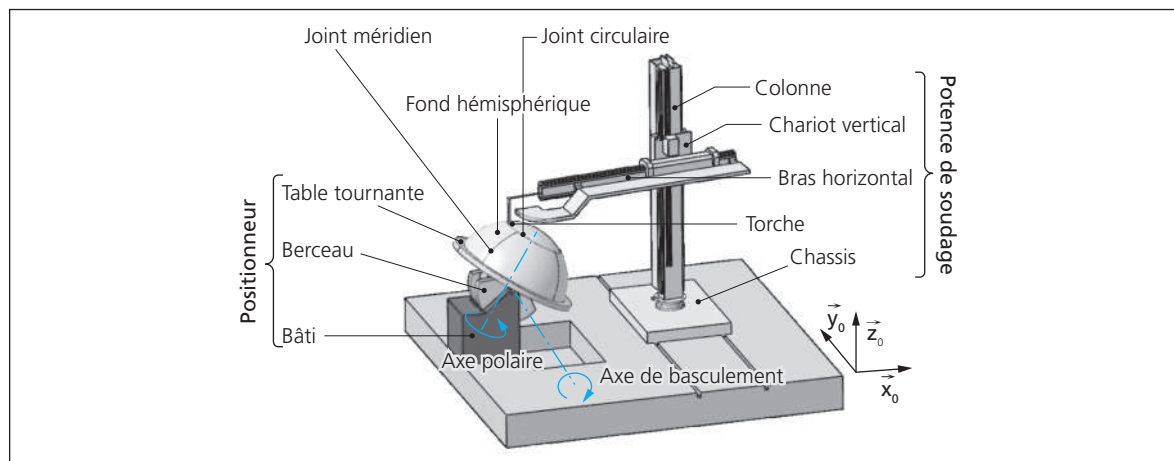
Vue générale de la machine de soudage automatisée
